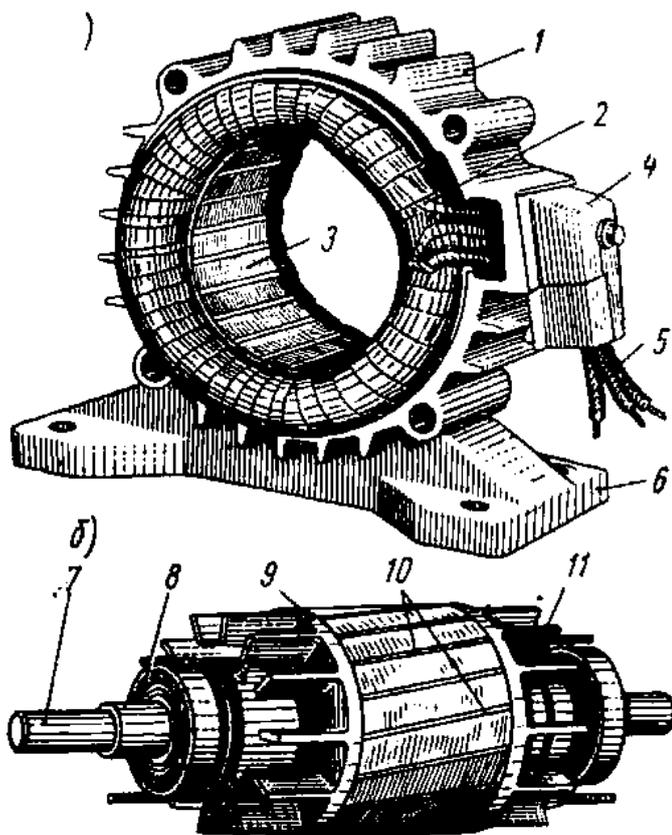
Статор (а) и ротор (б) однофазного асинхронного электродвигателя серии ЛОЛБ: 1 - станина; 2 - обмотка статора; 3 - пакет железа статора; 4 - коробка выводов; 5 - выводы; 6 - лапы; 7 - вал; 8 - подшипник; 9 - короткозамыкающее кольцо; 10 - стержни; 11 - вентиляционные лопасти
